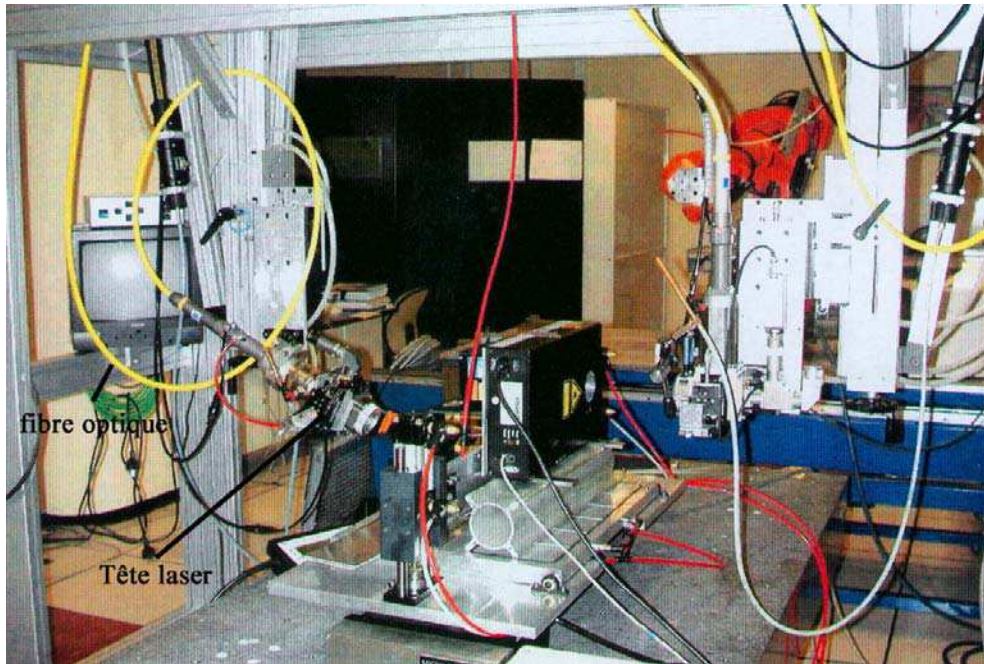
photo du dispositif de soudage (source EADS)
